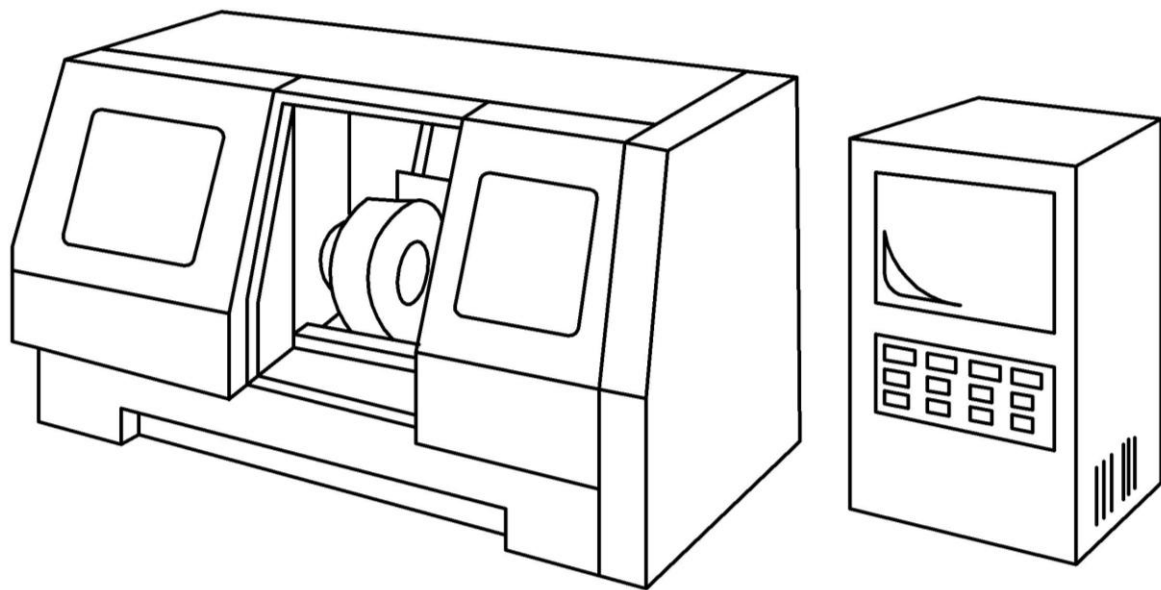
Загальний вигляд токарного верстата з ЧПК
